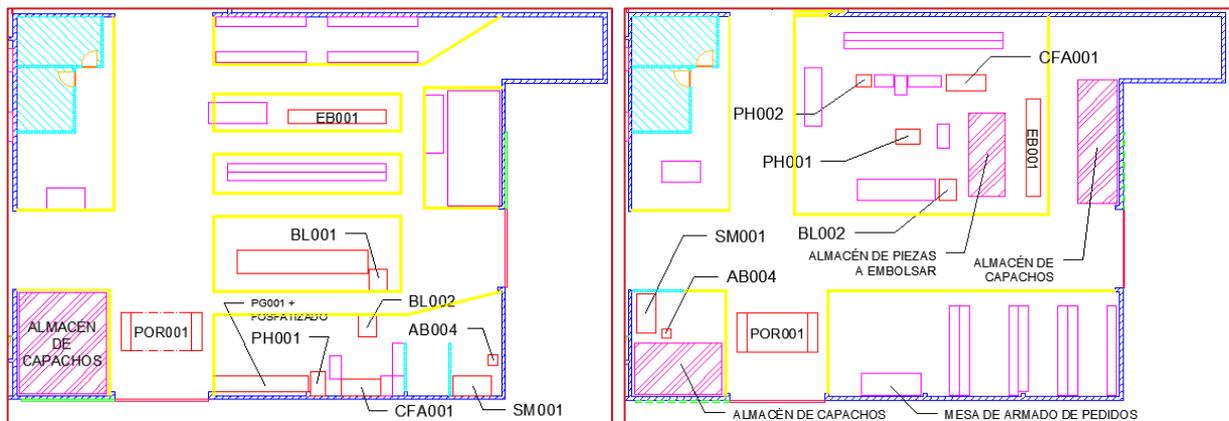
Layout actual (izquierda) y propuesto (derecha) del área de armado y despacho
